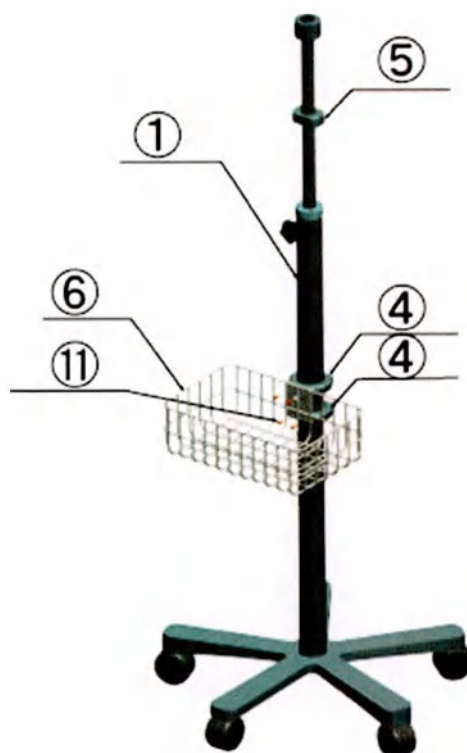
Установка корзины на телескопический штатив
